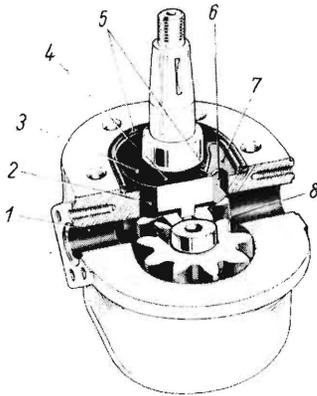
Schnitt durch die *Fesco-Piessey*-Pumpe.
